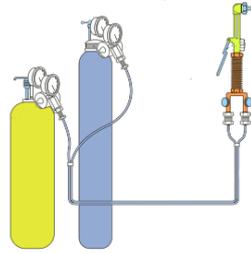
esquema de um equipamento de soldar OFW (Goodnight, 2018)
